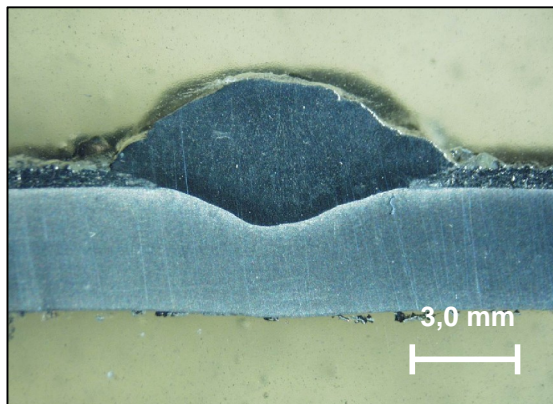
Macrografia de seção transversal de cordão de solda com eletrodo revestido AWS E309L sobre revestimento aspergido com arame de liga de Níquel AS-751 por AS com espessura de 0,50 mm. Energia de soldagem 6,5 kJ/cm. Ataque Villela.
